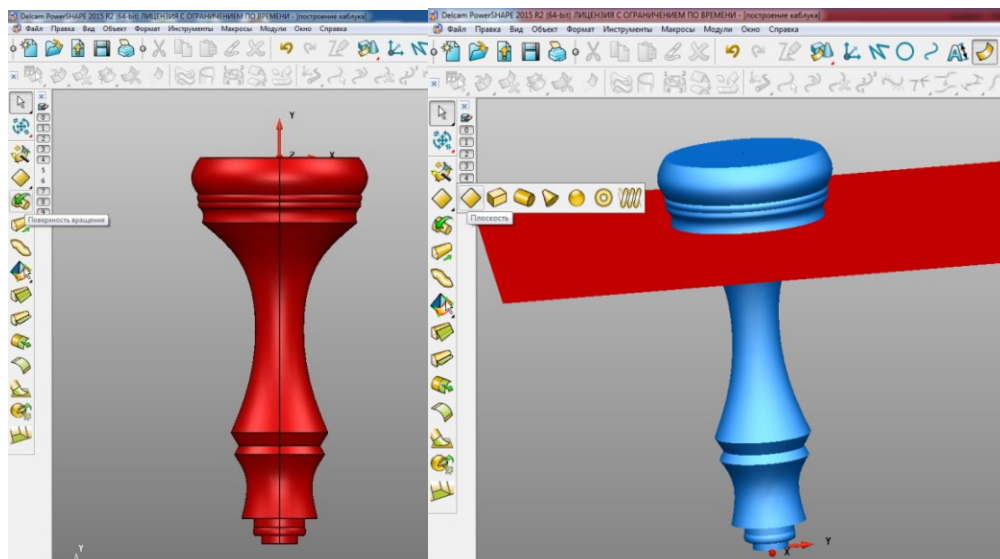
Моделювання заготовки для проектування каблука та розрізання її на дві частини
